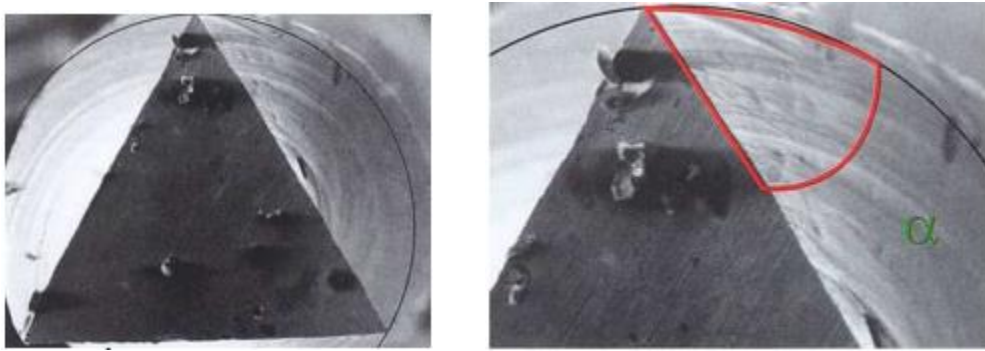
Ángulo de corte del ensanchador visto transversalmente. ¹¹
